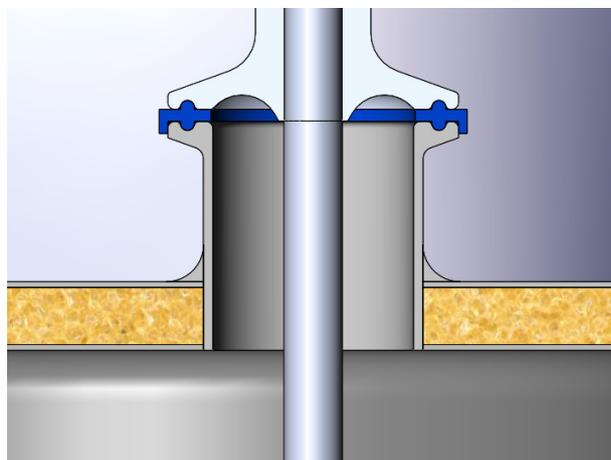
Soldado a ras en el interior y pulido
